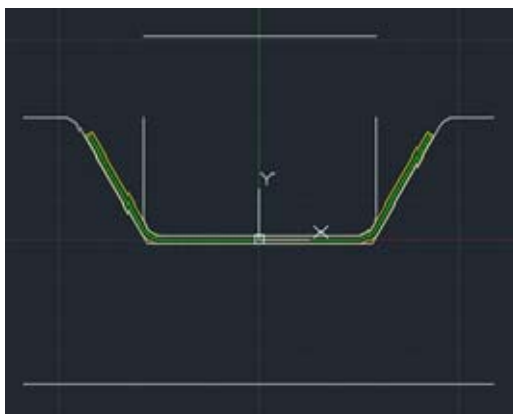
Пример профиля рабочей поверхности формующего ролика
